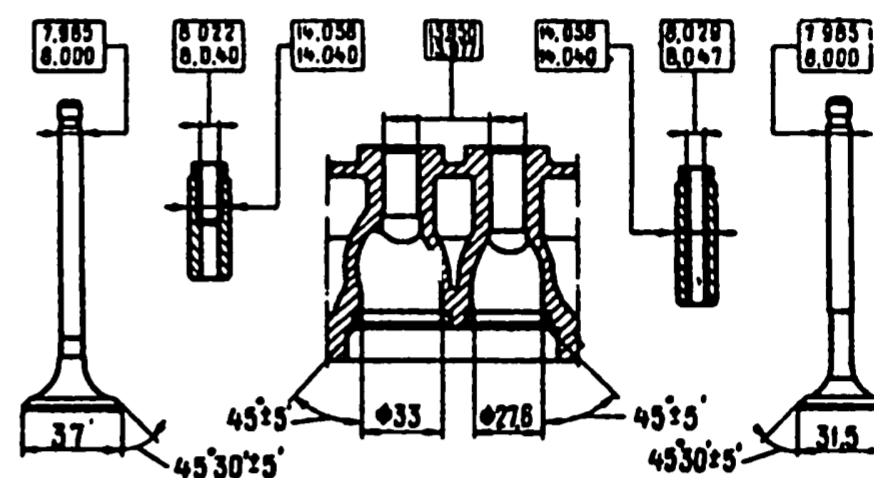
Основные размеры клапанов и направляющих втулок
